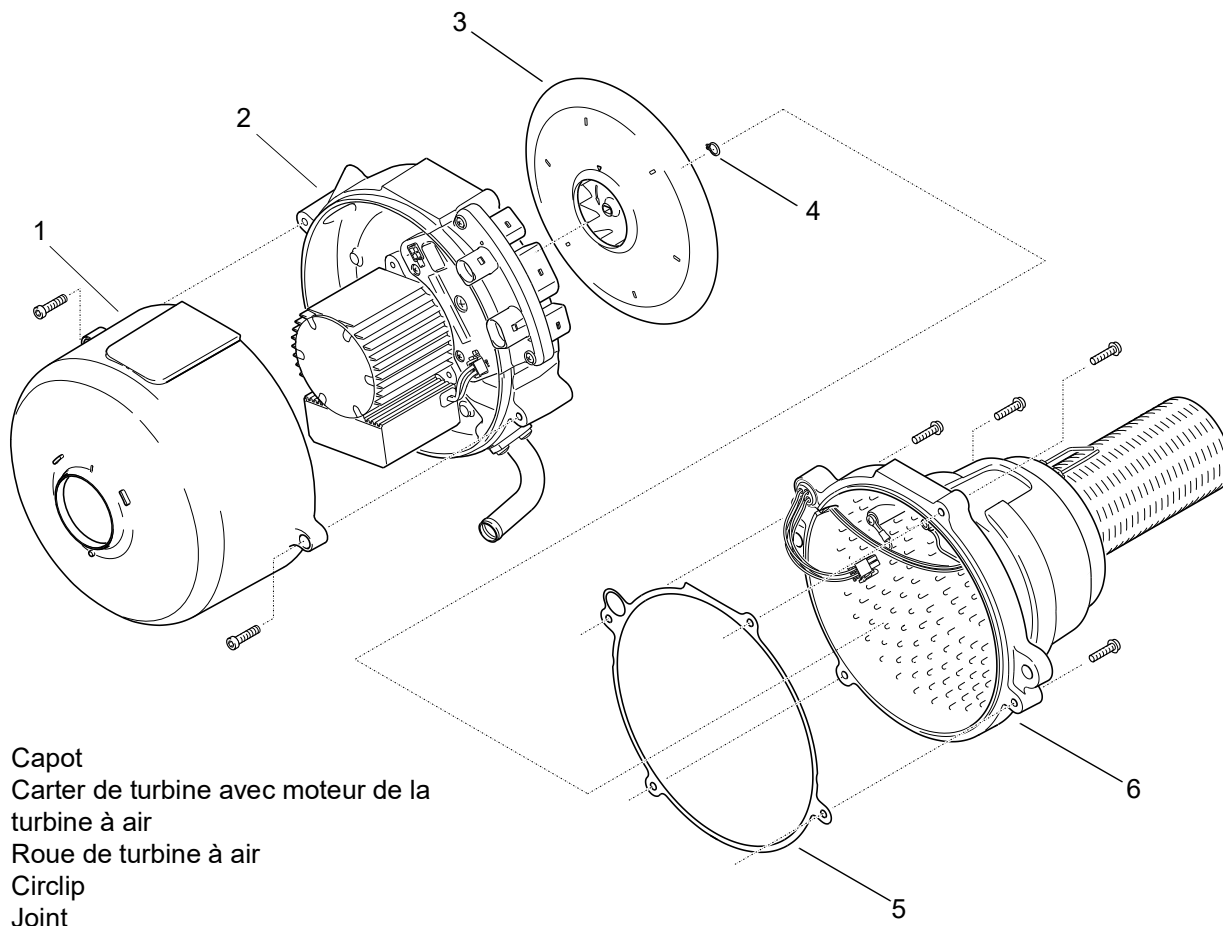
Séparation du carter de turbine de la chambre de mélange
